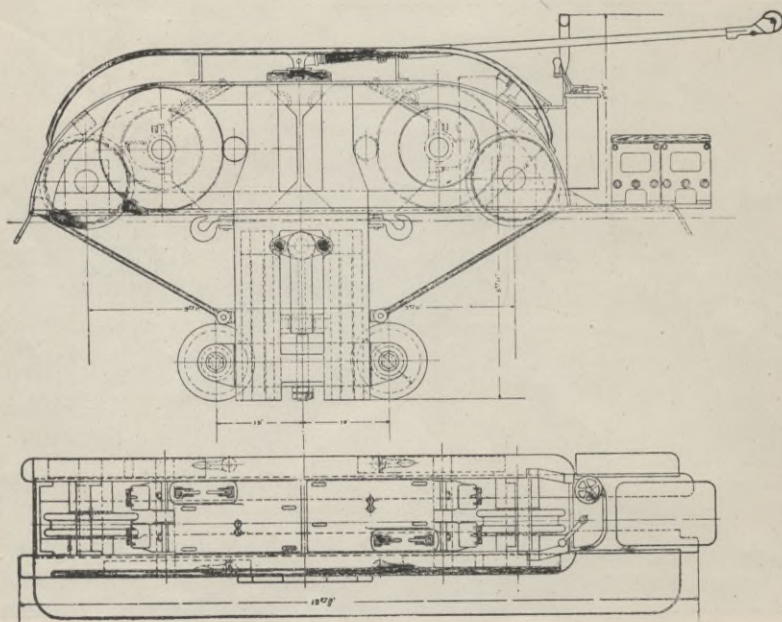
Aufriss und Grundriss einer 100 pferdigen elektrischen Treidellokomotive.
